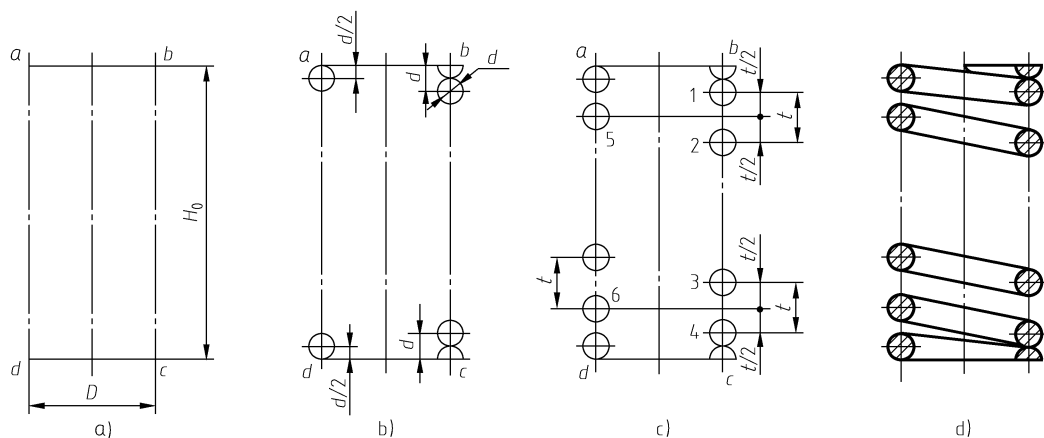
圆柱螺旋压缩弹簧的具体绘图步骤
